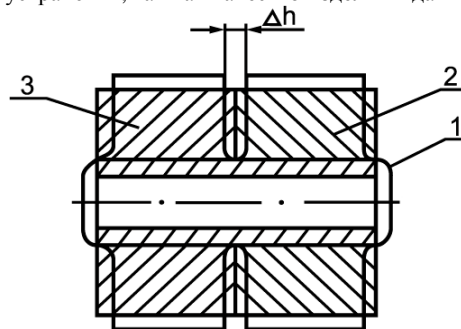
Многоэлементное соединение деталей с натягом и схема деформаций деталей при КТСС: 1 – охватываемая деталь; 2 и 3 – охватывающие детали
